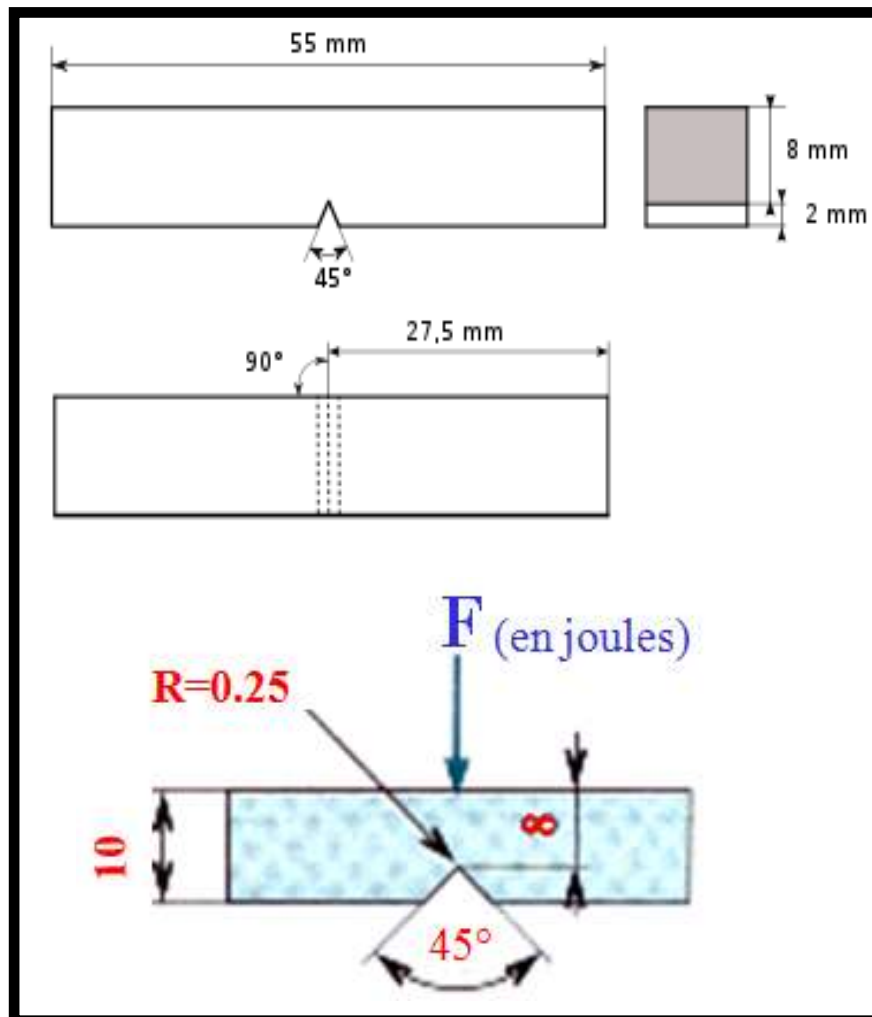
Dimensions et forme de l'éprouvette Charpy en V.
